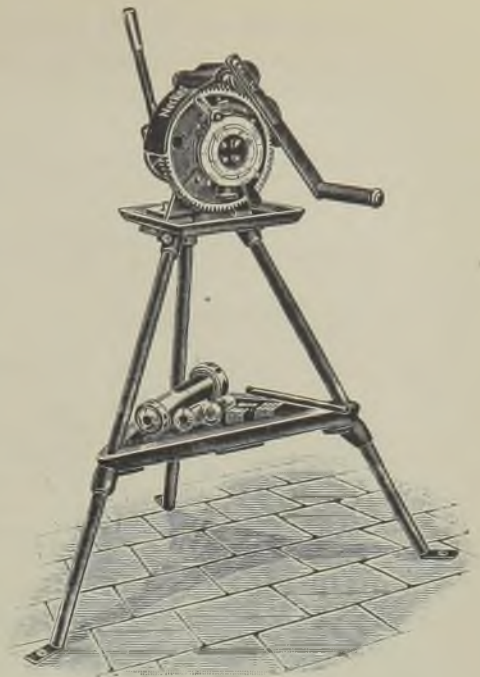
Gewinbeschneidmaschine „Nedar“ mit Handbetrieb für Außengewinde bis 50 mm und 100 mm. (Delisle & Ziegele, Stuttgart.)
